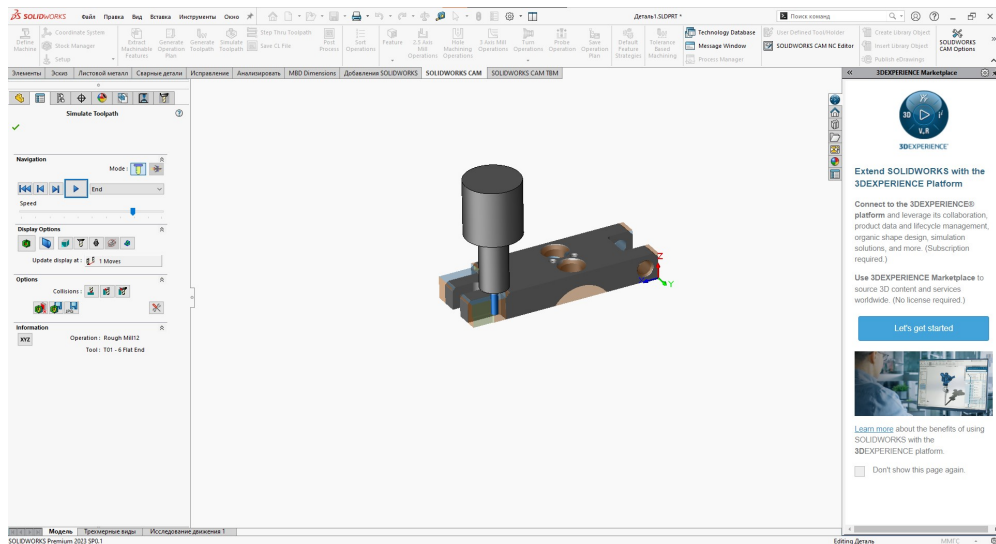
Симуляція фрезерування бокової поверхні
